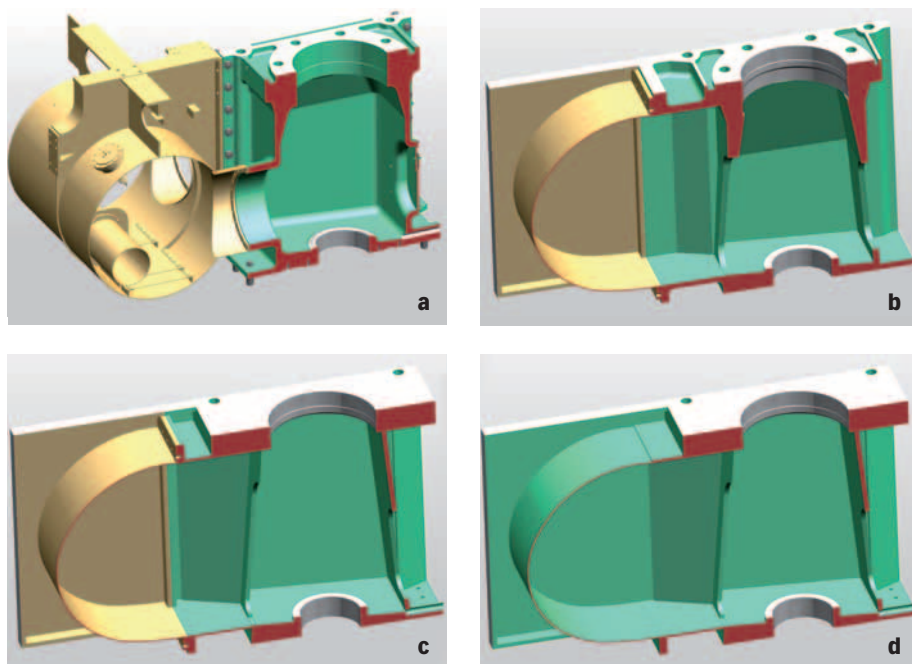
(von a nach d): Konventioneller Zylinderblock in Gussausführung mit Spülluftbehälter; neuer Zylinderrahmen in der gegossenen Ausführung mit angeschraubtem D-förmigen Spülluftbehälter; neuer Zylinderrahmen in der geschweißten Ausführung mit angeschraubtem D-förmigen Spülluftbehälter – derselbe D-förmige Spülluftbehälter für die gegossene und die geschweißte Ausführung; Zylinderrahmen in geschweißter Ausführung mit integriertem D-förmigen Spülluftbehälter
